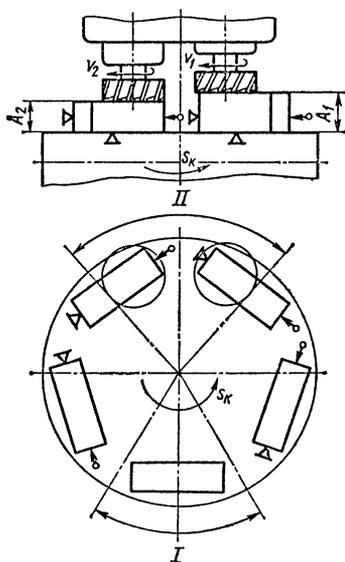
Схема обработки поверхностей на карусельно-фрезерном станке
